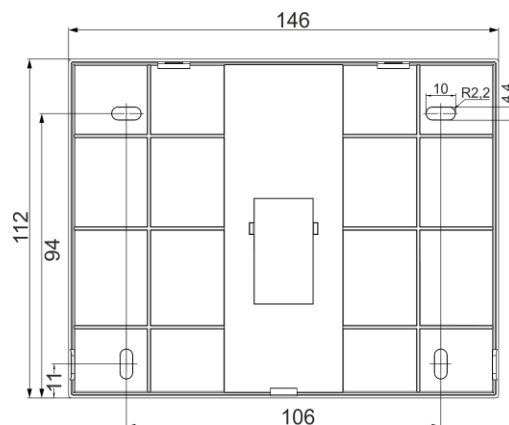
Установочный чертеж основания корпуса ВПУ-A24/700
